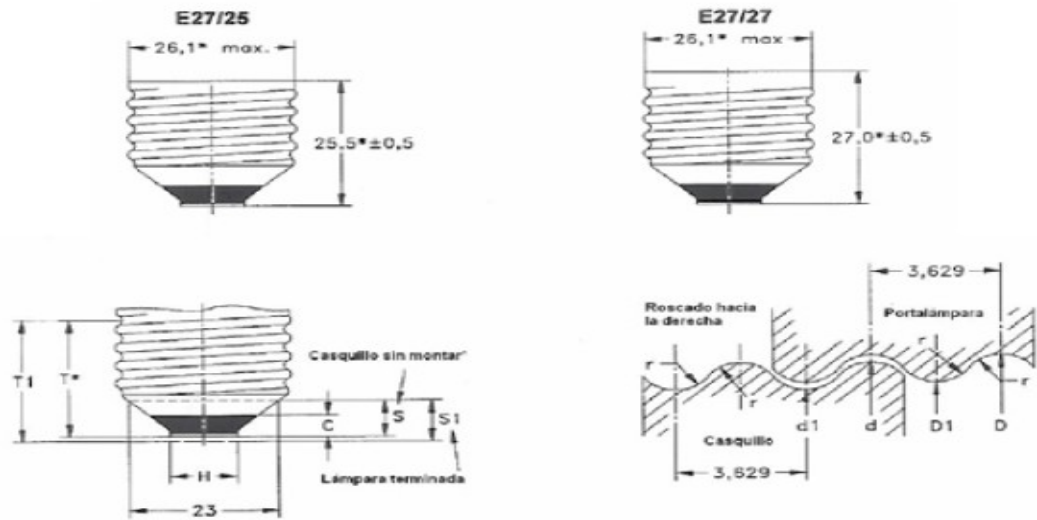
Dimensiones del casquillo de una bombilla en milímetros.
